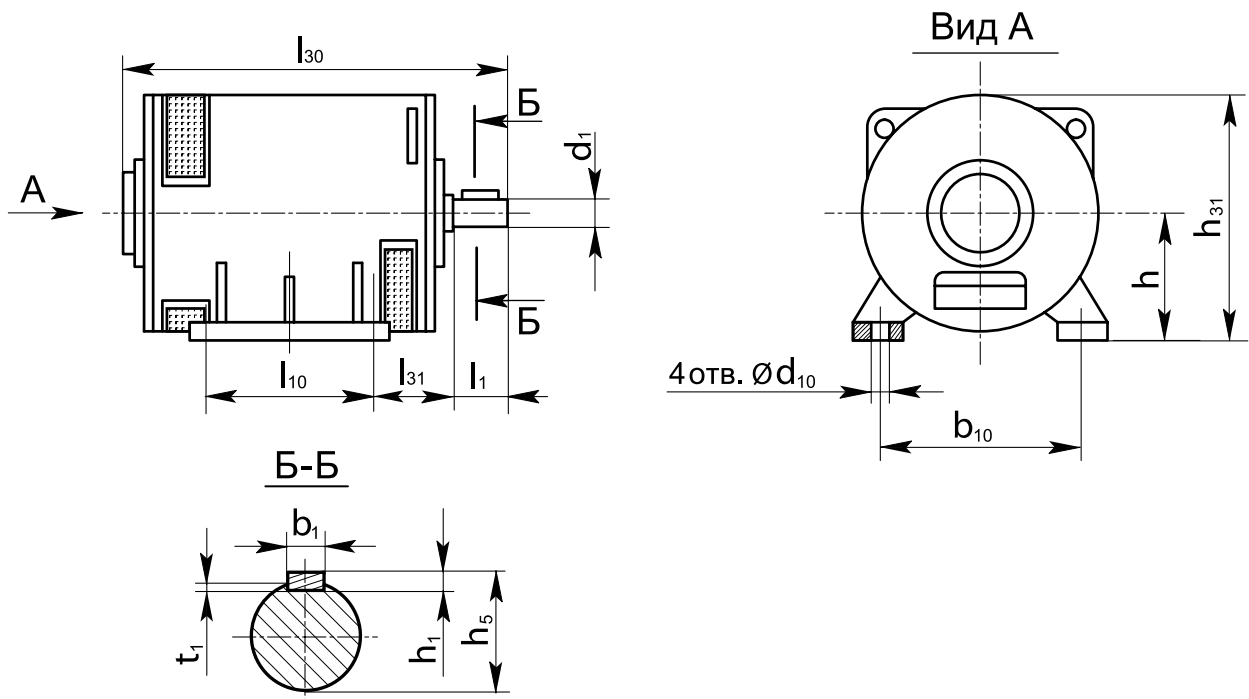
Габаритные, установочные и присоединительные размеры электрических машин типа ПМ91–ПМ112
